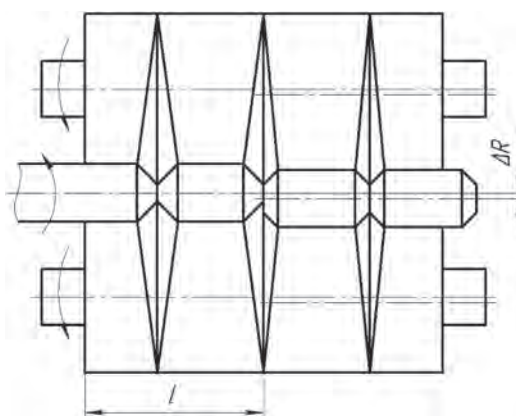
Сборный инструмент для разделения прутков поперечно-клиновой прокаткой
